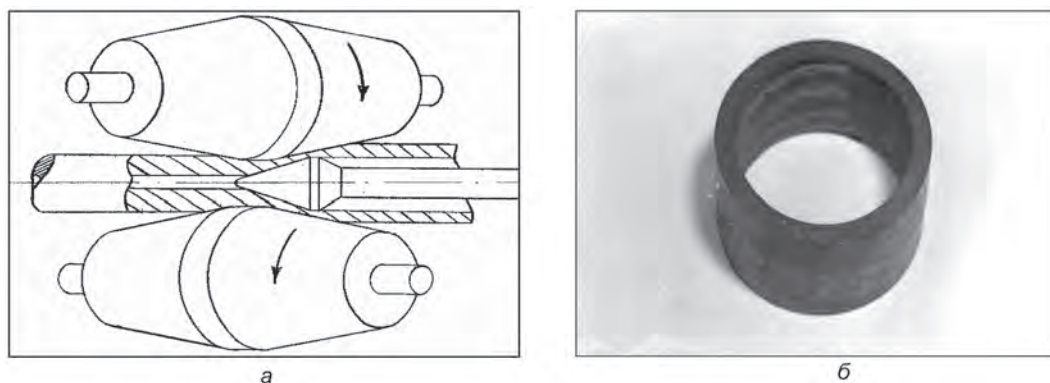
Получение деталей типа гильз цилиндров винтовой прокаткой-прошивкой: а – схема процесса; б – заготовка гильзы цилиндра из чугуна
